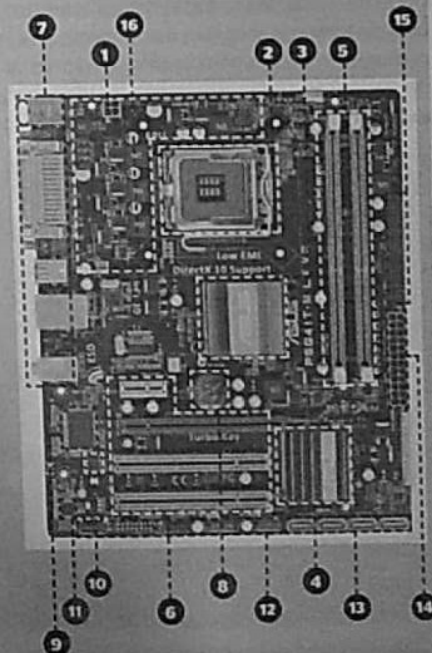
PCB de un motherboard moderno, que puede llegar a tener entre ocho y diez capas intermedias para la interconexión de los componentes soldados a él.
